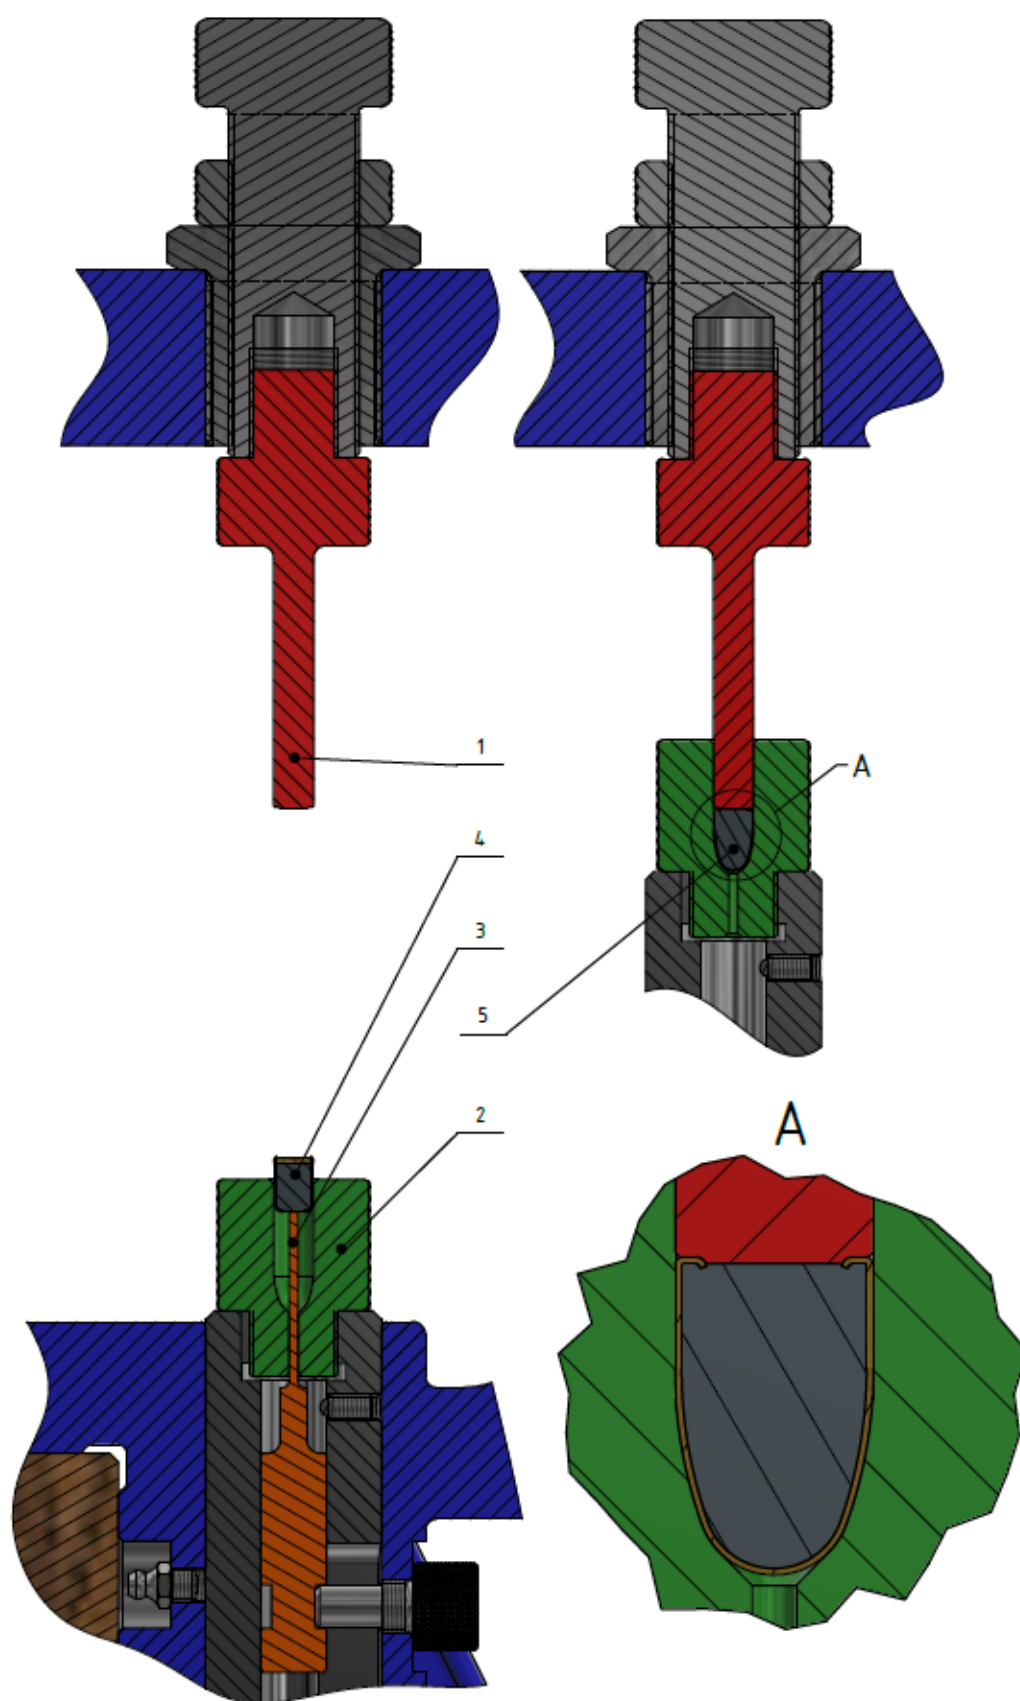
Vyobrazení nástrojů pro usazení a lemování v rozpadu
